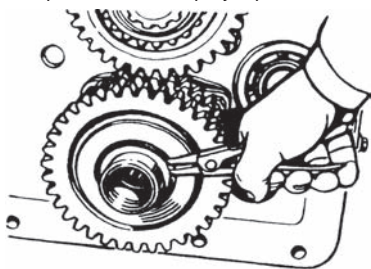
Спрессовка промежуточной шестерни понижающего редуктора, замена подшипников № 212.
